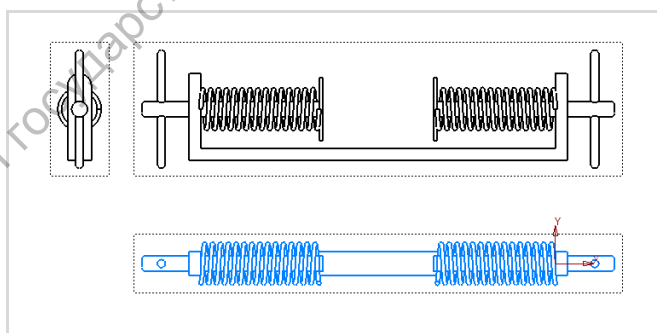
Ассоциативный чертеж, выполненный для трехмерной модели детали «Ручной пресс»
